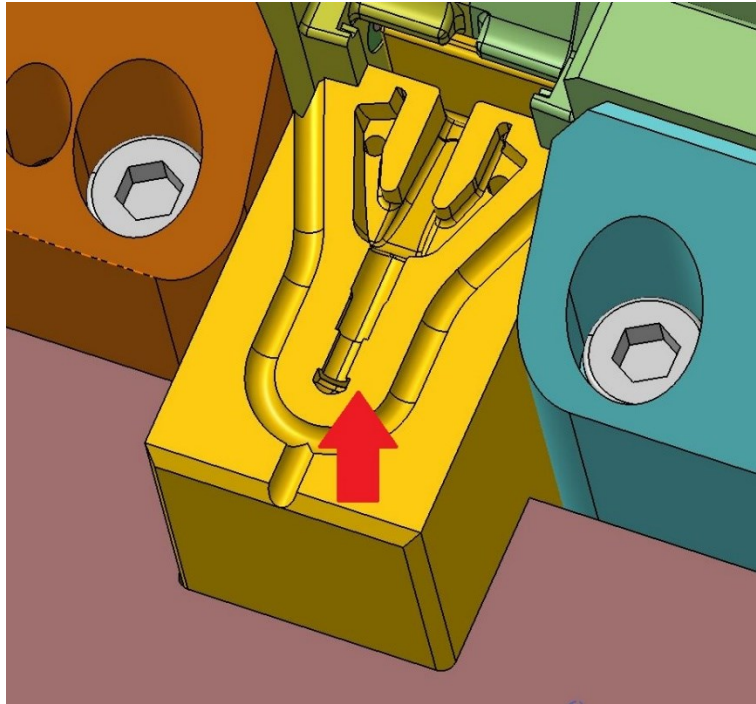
Hotový výrobek z hloubené dutiny ve tvárnici
